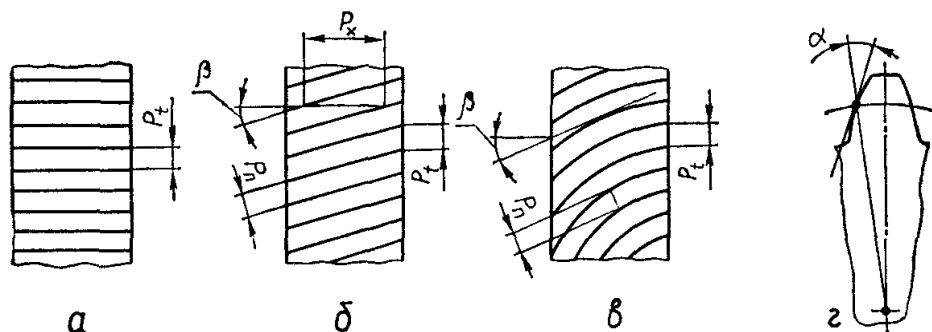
Форма та розміщення зубців зубчастих коліс
